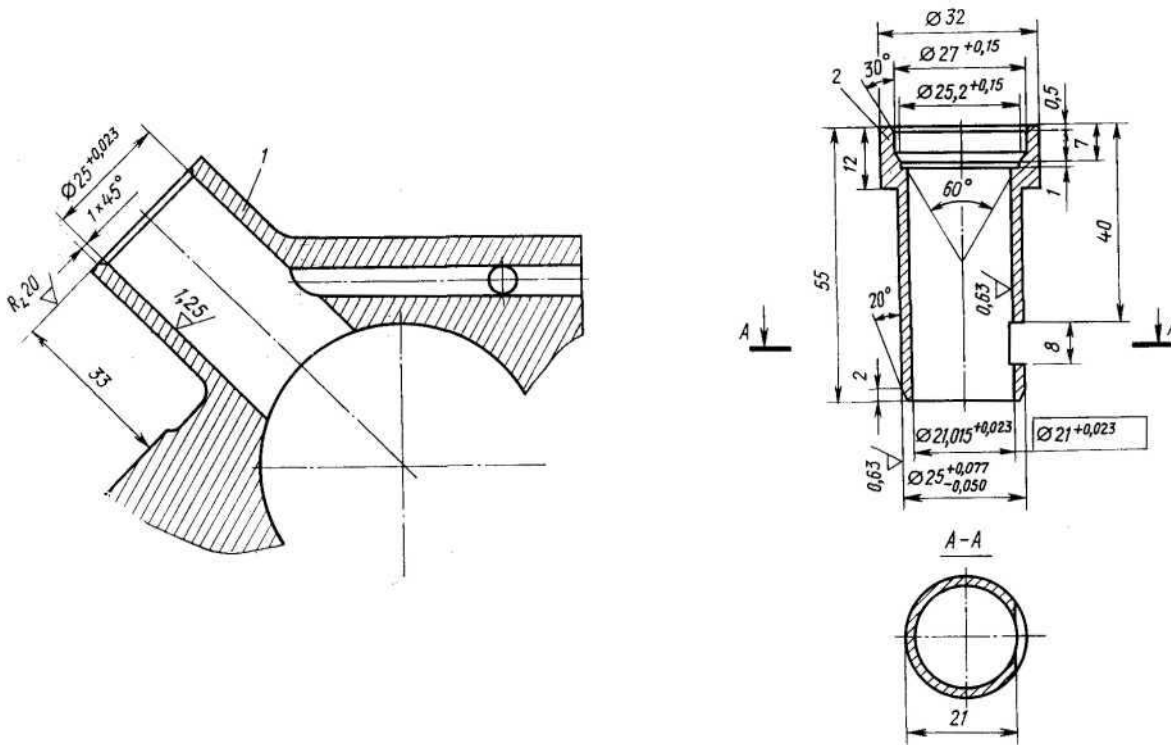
Расточка картера двигателя под ремонтные втулки бонок толкателя:
